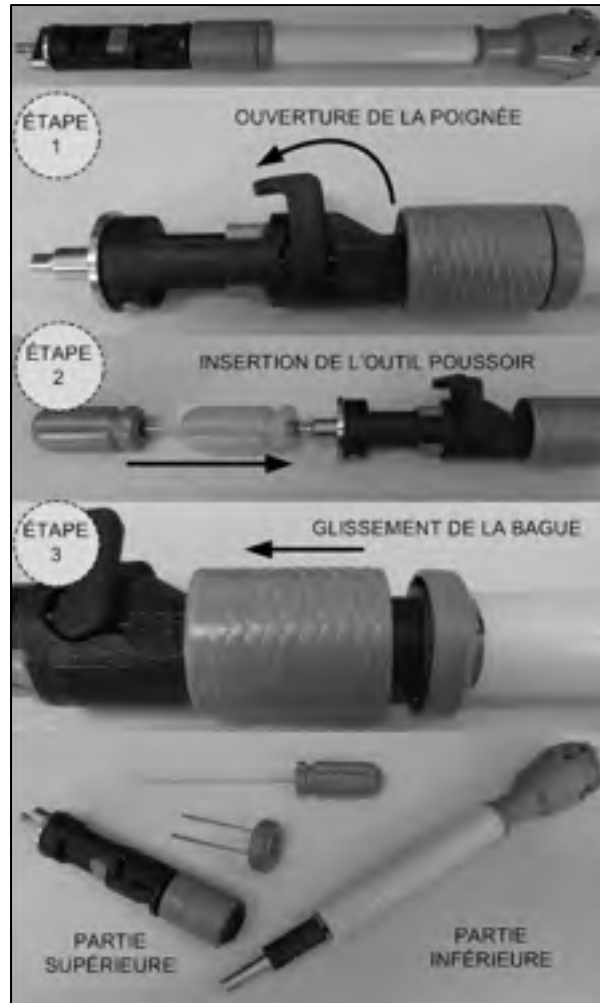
Étapes de désassemblage de l'ADV – prototype conceptuel
